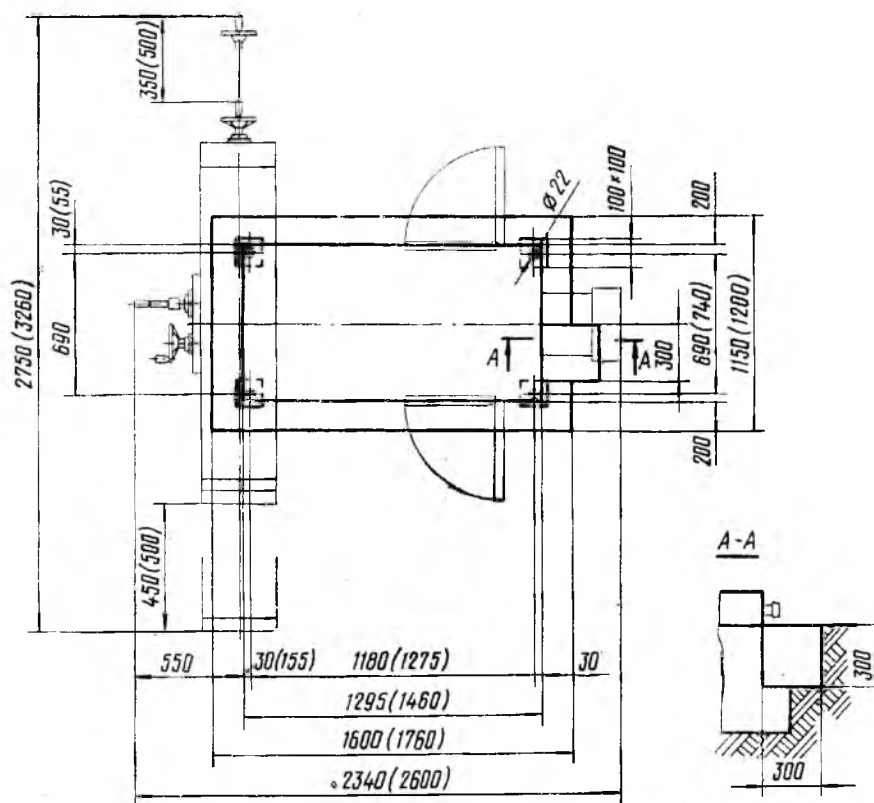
Установочный чертеж станков 6P12Б, (6P13Б)
